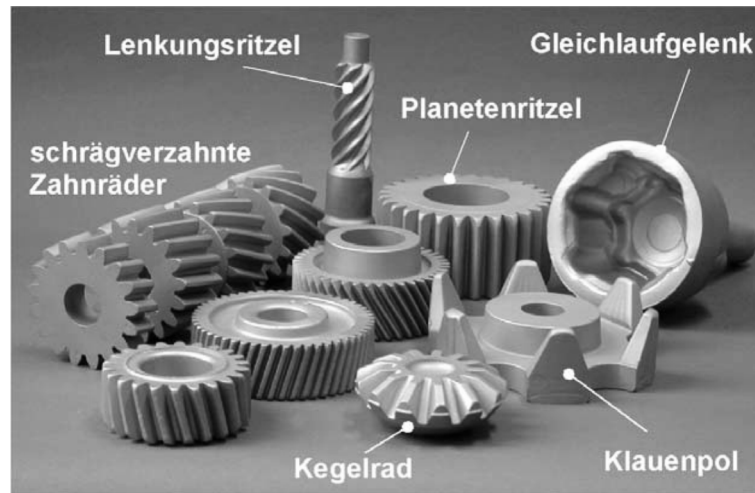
Beispiele für präzisionsgeschmiedete Bauteile [Beh06]; © Institut für Umformtechnik und Umformmaschinen (IFUM)
